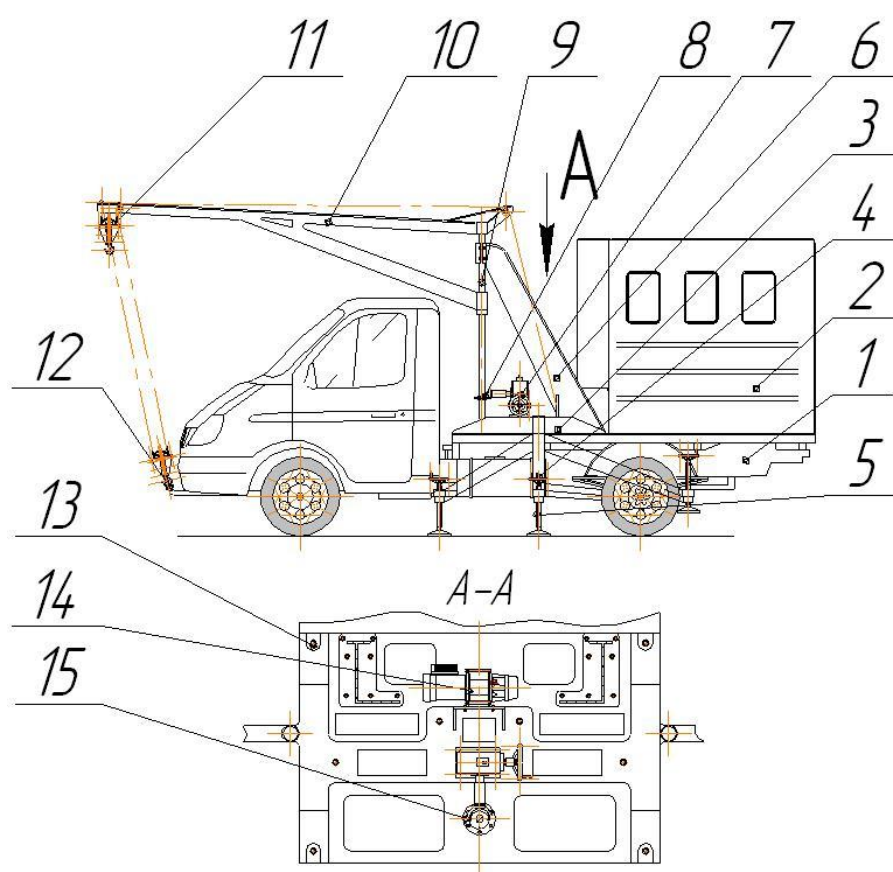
Устройство мобильного агрегата технического обслуживания
